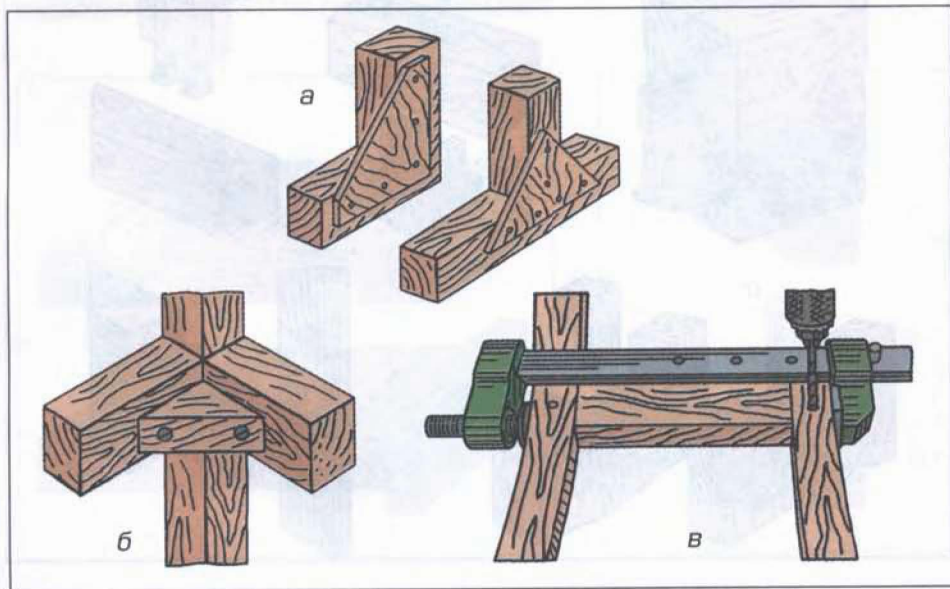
Укрепление соединений деталей мебели в стыковочных узлах: а – косынками из фанеры, б – бобышками, в – деревянными нагельями
